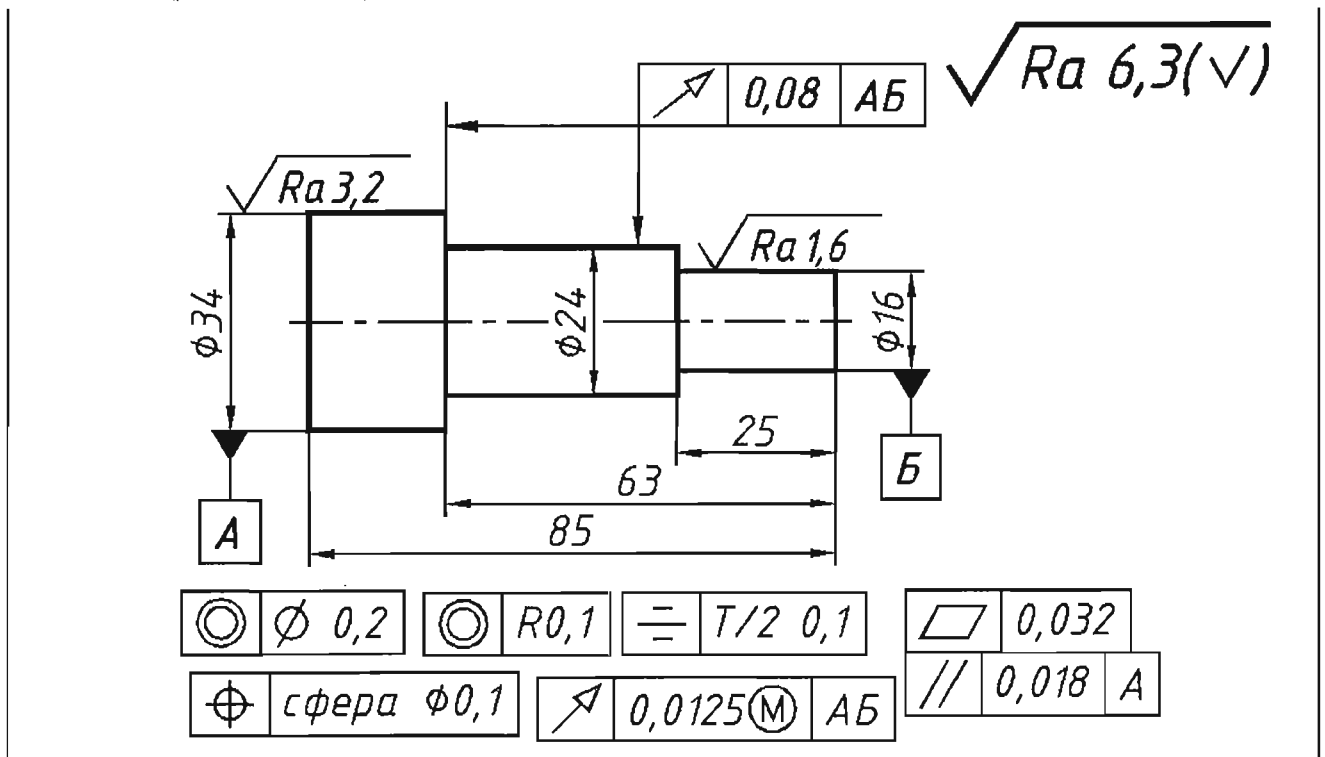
Чертеж вала. Допуски формы и расположения поверхностей
